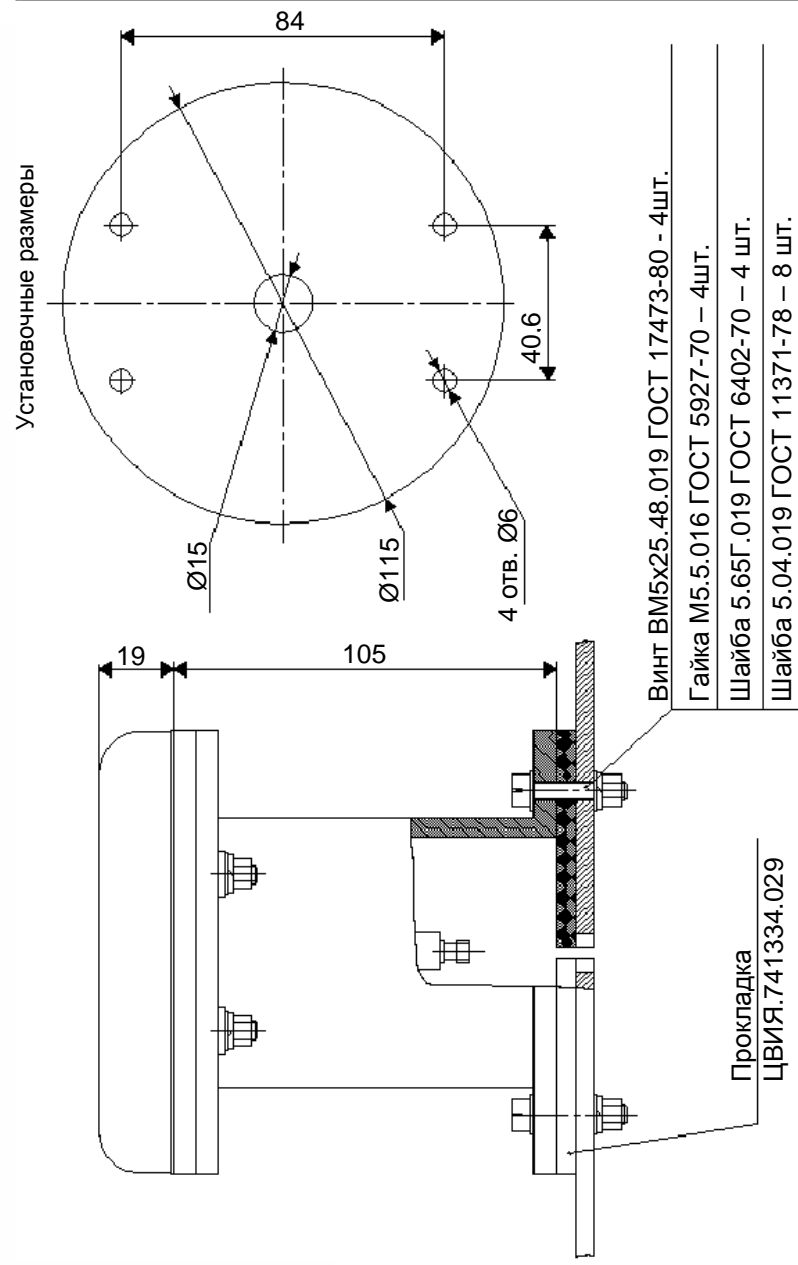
Общий вид АУУ-1С и установочные размеры для исполнения ЦВИЯ.468731.001
